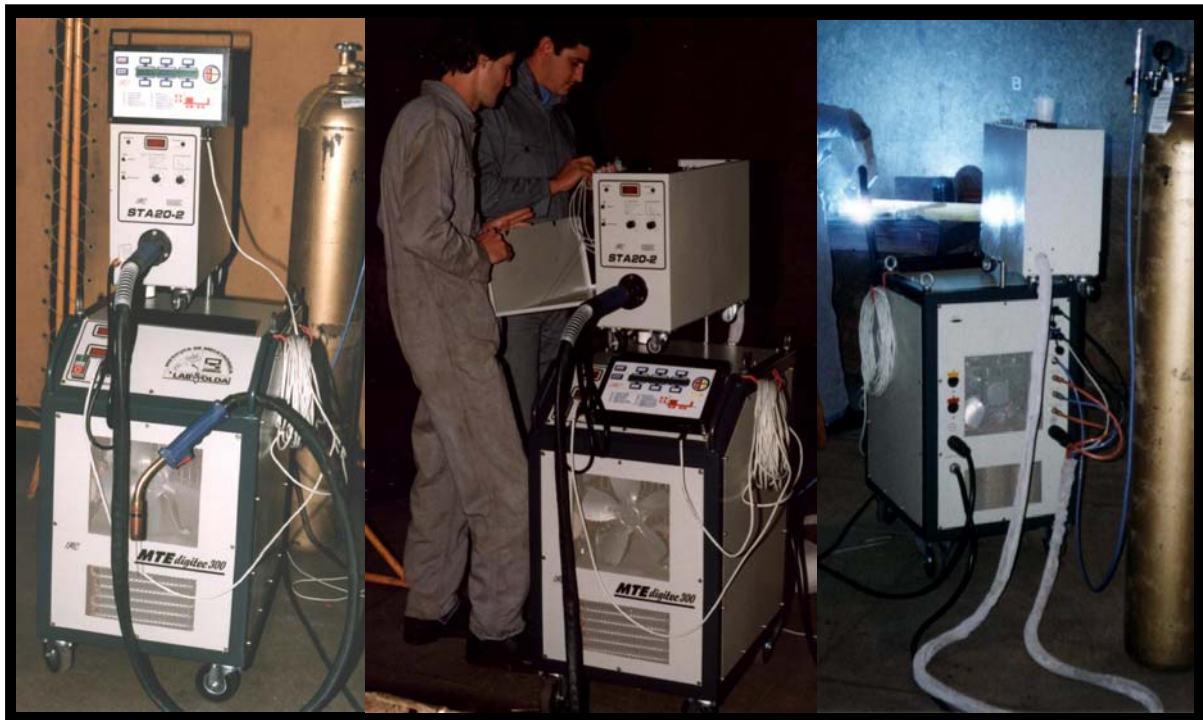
Versão do equipamento de soldagem para soldagem de turbinas.
